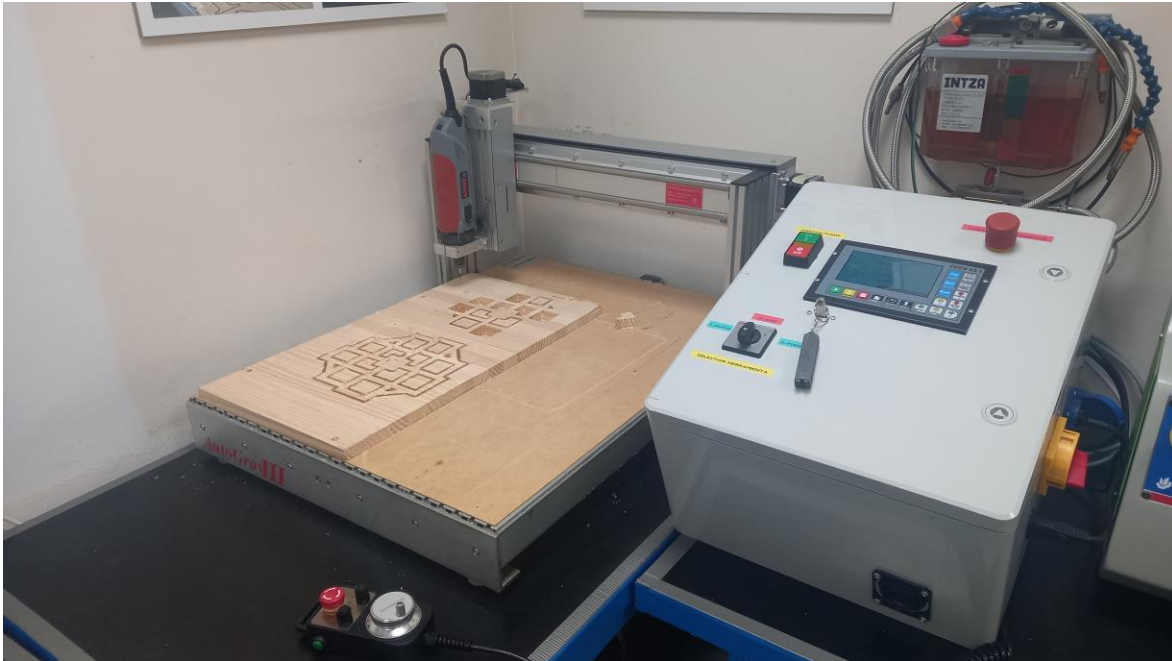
Montaje para la realización del ensayo. (Elaboración propia)
